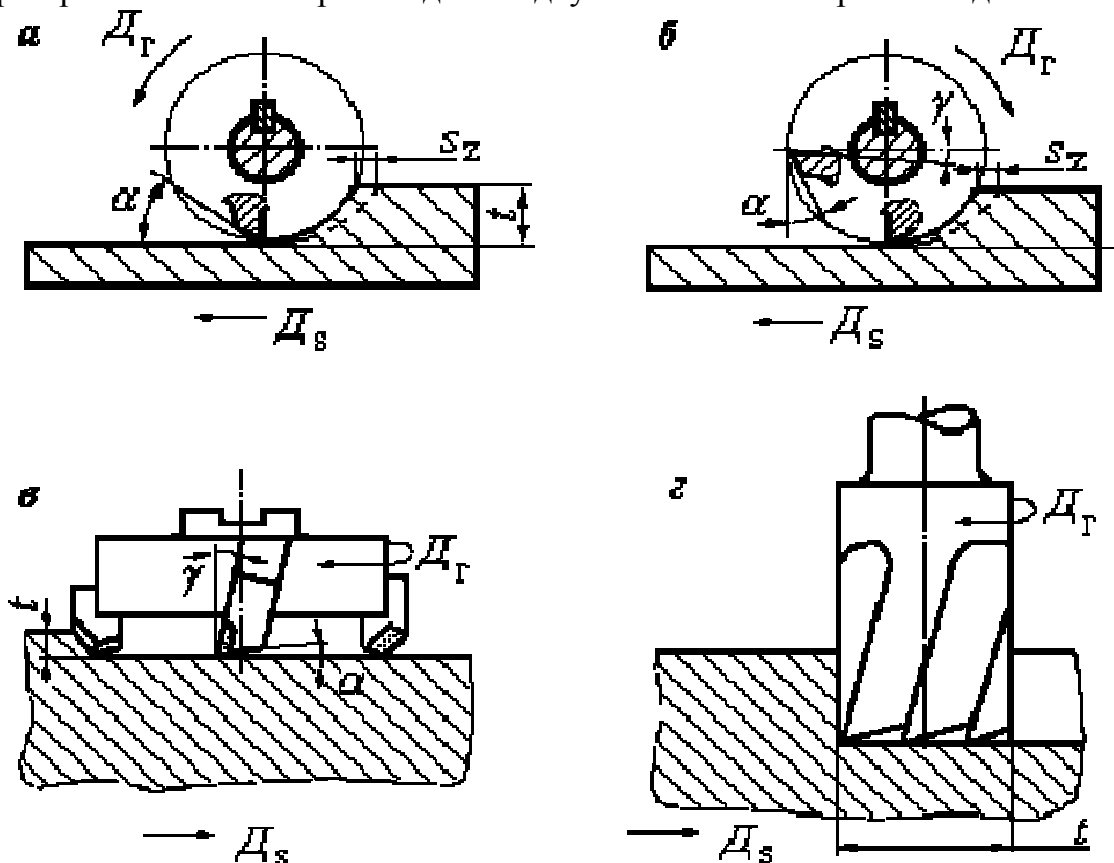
Виды фрезерования: а) – против подачи, б) – по подаче, в) – торцевой фрезой, г) – концевой фрезой.
